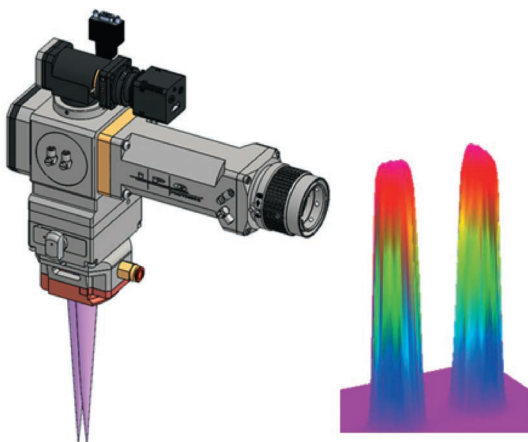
Внешний вид сварочной головки IPG FLW D50 с модулем двойного фокуса [5]
